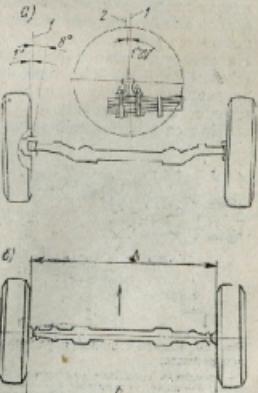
Развал колес, поперечный наклон шкворней и схождение колес:
